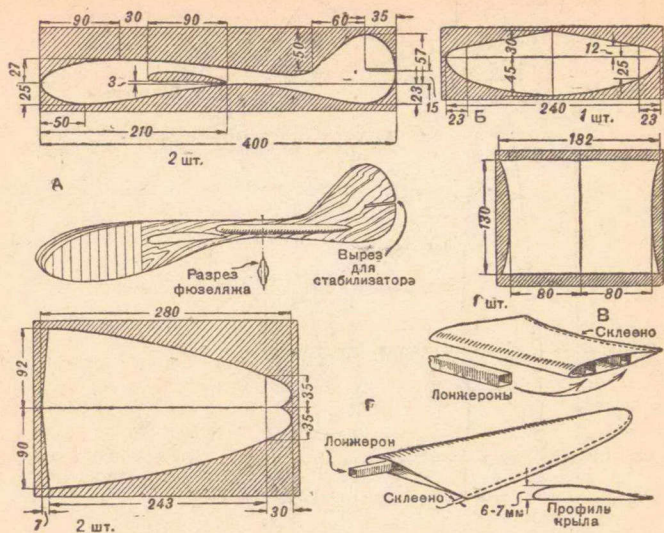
Детали модели: А — фюзеляж, Б — стабилизатор, В — центроплан, Г — консоль.
